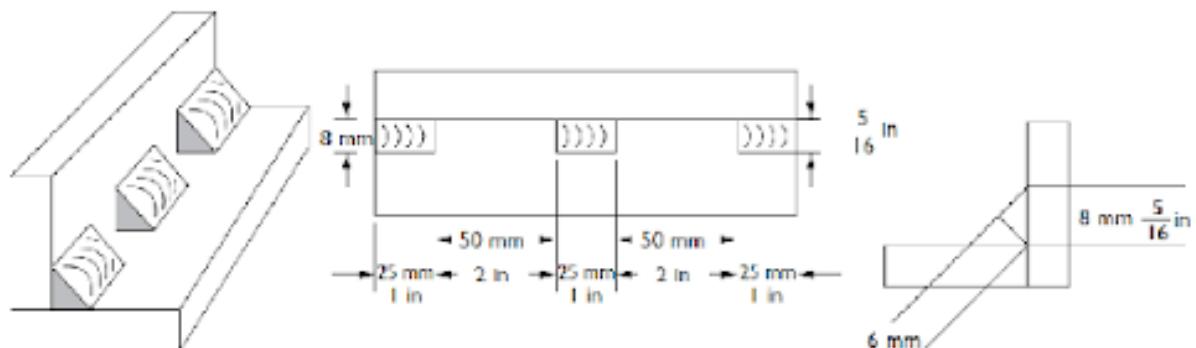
Элементы, которые могут быть использованы в обозначении сварного шва
